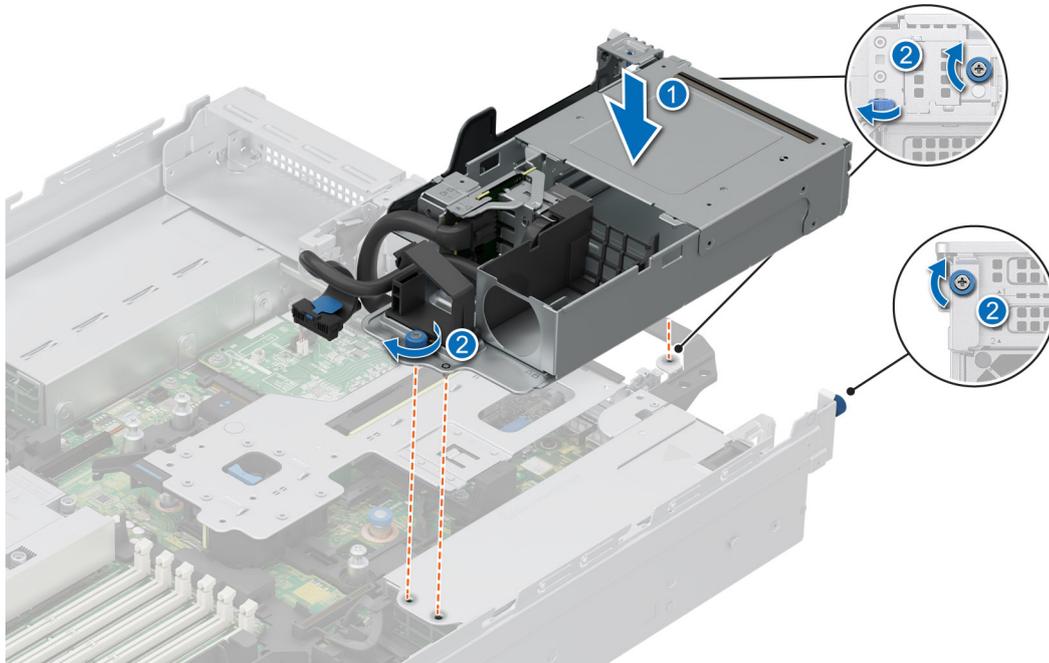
Installation du module de 4 disques arrière EDSFF E3.S
